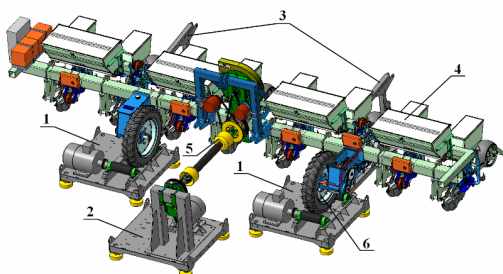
Общий вид стенда для технического обслуживания и настройки сеялок точного высева: 1 – блок электропривода опорно-приводного колеса; 2 – блок электропривода вентилятора; 3 – опорные регулируемые стойки; 4 – сеялка точного высева; 5. - карданный приводной вал; 6. – опорное приводное колесо.
